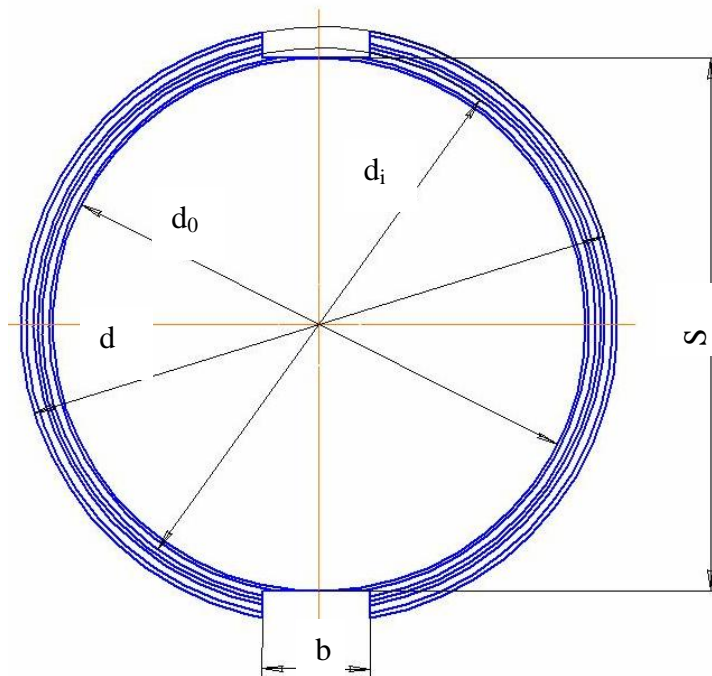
Схема срезания припуска протяжкой с двумя шпонками
